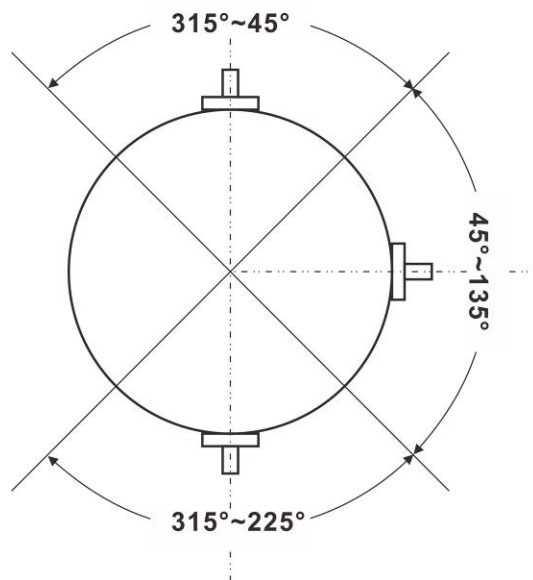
J-L045 倾斜 45° 向下焊接位置
